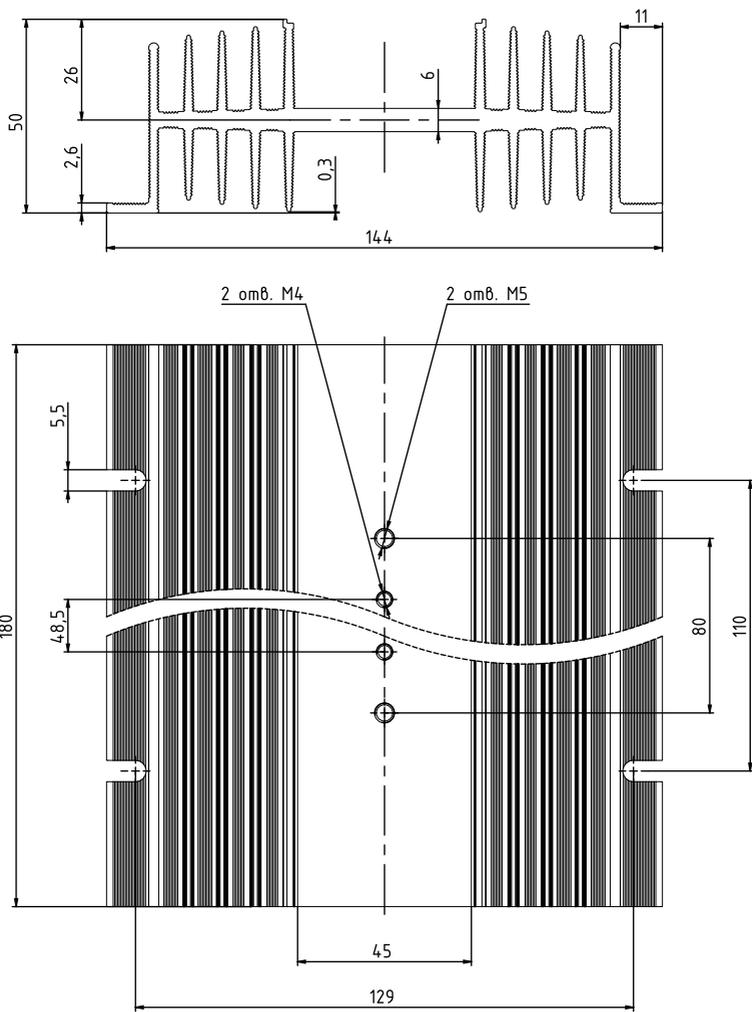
Габаритные размеры радиатора РТР063.1
